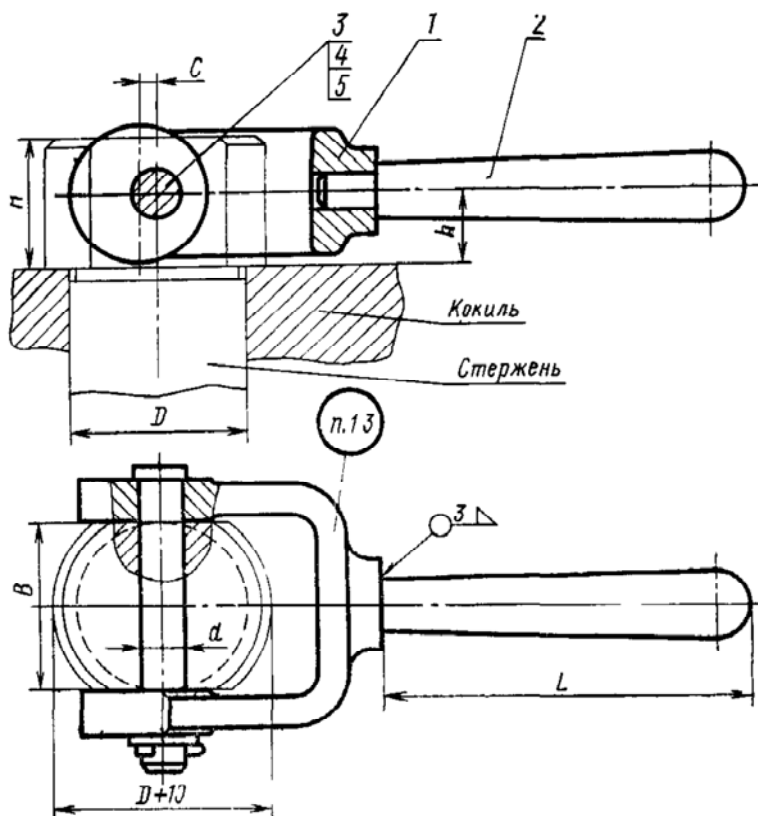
Приспособление для удаления стержней эксцентриковой скобой
